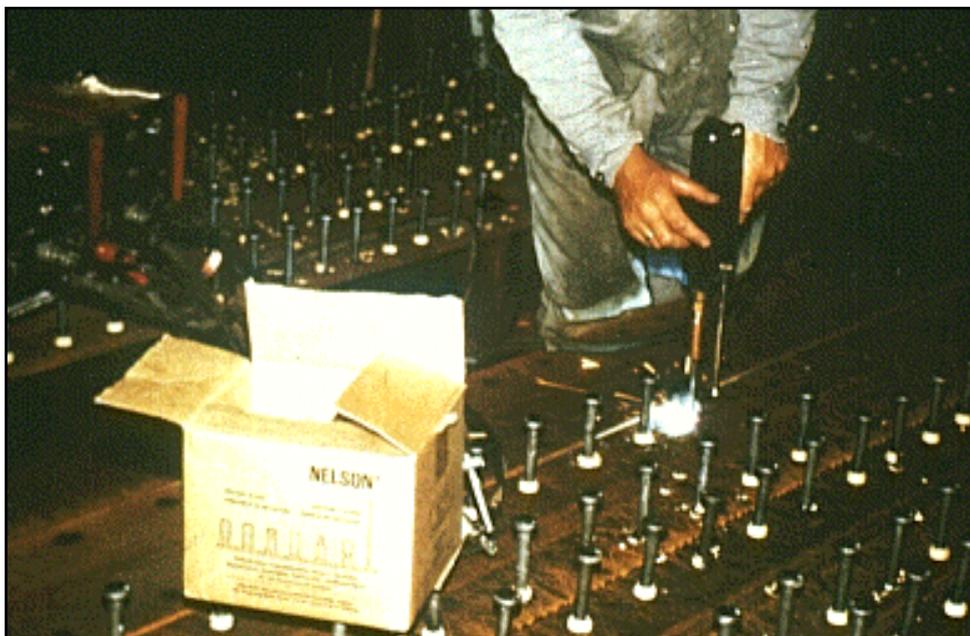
exemple de mise en place de goujons sur des poutres en atelier.
